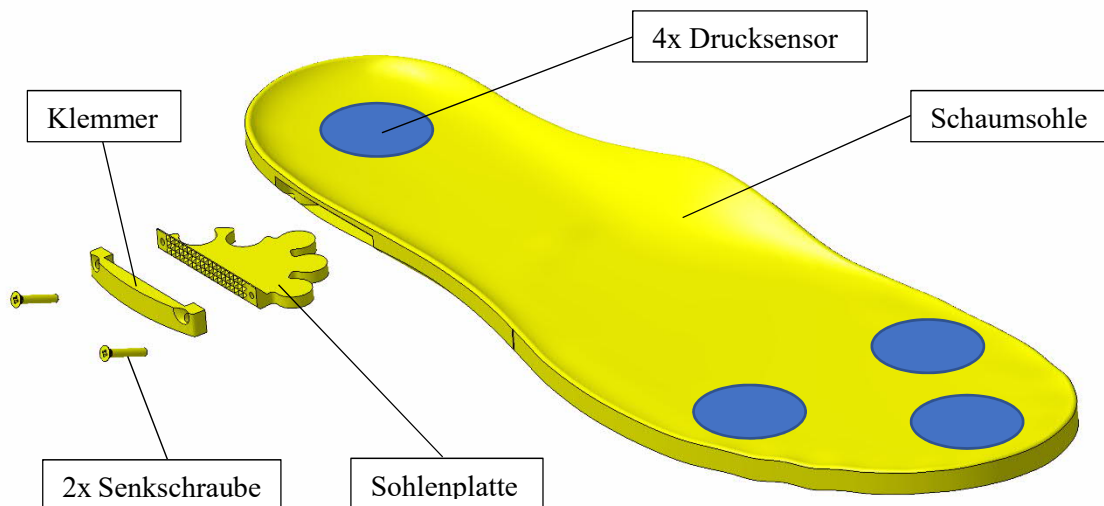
Isometrische Explosionsansicht der Sohle; die vier Positionen (Ferse, Fussballen innen und aussen, Zehen) der Drucksensoren im Sohleninnern wurden mit blauen Punkten markiert
